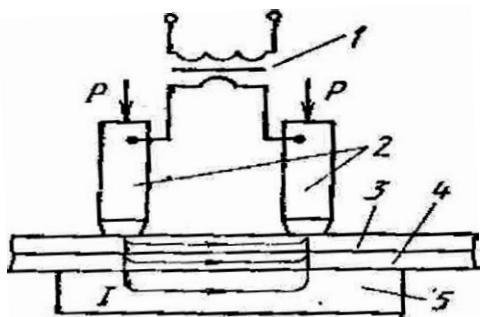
Односторонняя точечная сварка: 1 - сварочный трансформатор; 2 - электроды; 3 -
